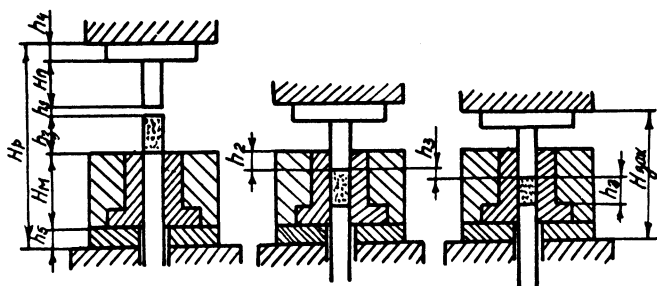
Схема горячей допрессовки изделий в закрытом штампе прессы
